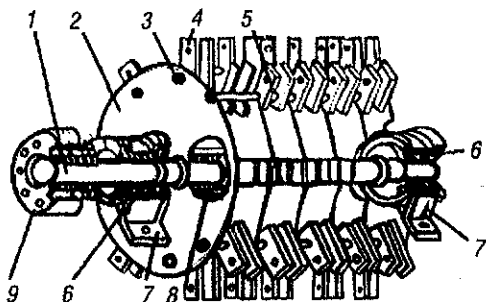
Схема ротора дробилки ДБ-5: 1 – вал; 2 – диск; 3 – ось; 4 – молоток; 5 – распорная втулка; 6 – двухрядный роликоподшипник; 7 – корпус; 8 – втулка; 9 – муфта
